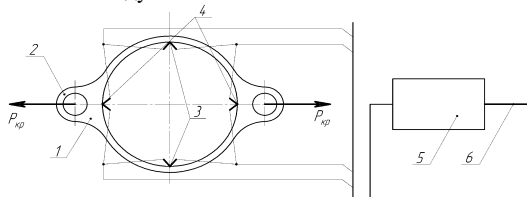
Тензодатчик для вимірювання тягового опору: 1 – металевий корпус датчика; 2 – вуха; 3 – тензорезистори розтягування; 4 – тензорезистори стиску; 5 – мікроконтролер; 6 – CAN-шина
